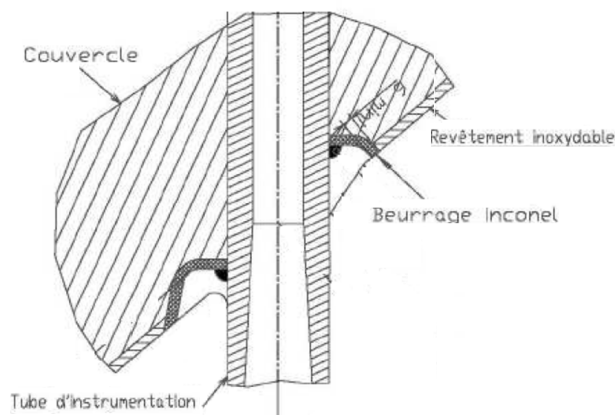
schéma d'une soudure d'adaptateur
